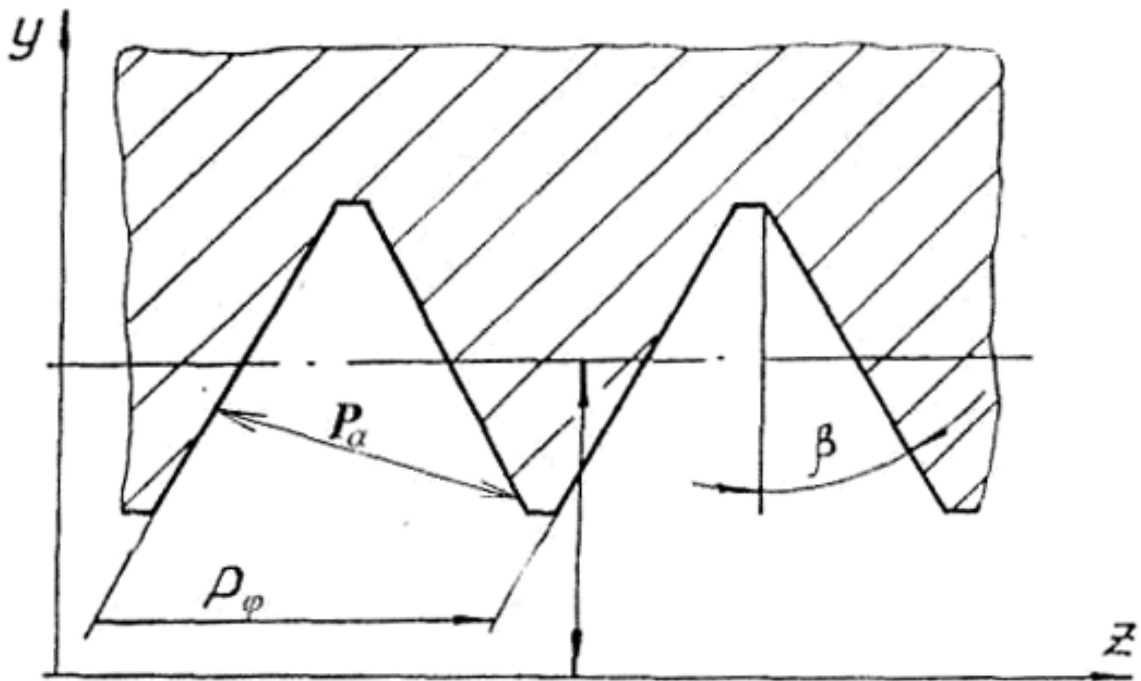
Геометрия винтовой поверхности резьбы жесткого элемента
